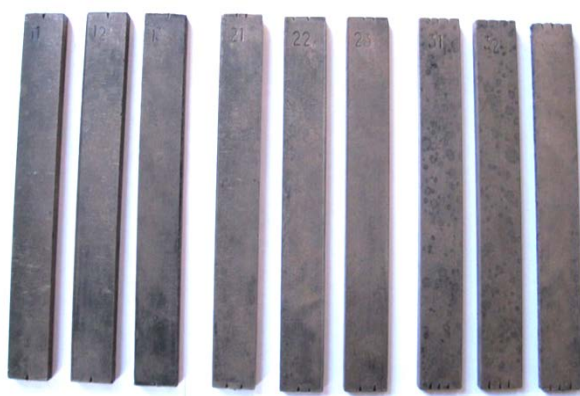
Пластини струмоприймачів електровозів, виготовлені методом порошкової металургії (загальний вигляд).
